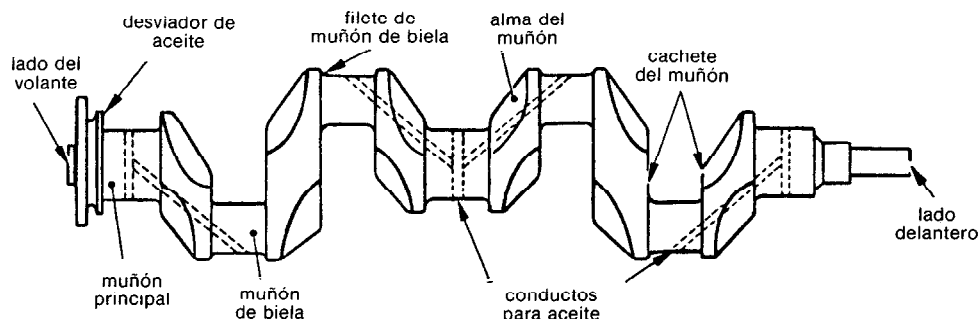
Cigüeñal para motor de cuatro cilindros con tres cojinetes principales; se mencionan las partes principales
